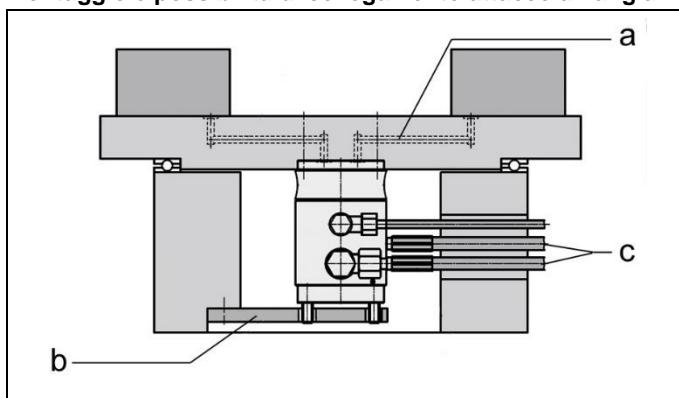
Montaggio e possibilità di collegamento attacco a flangia
